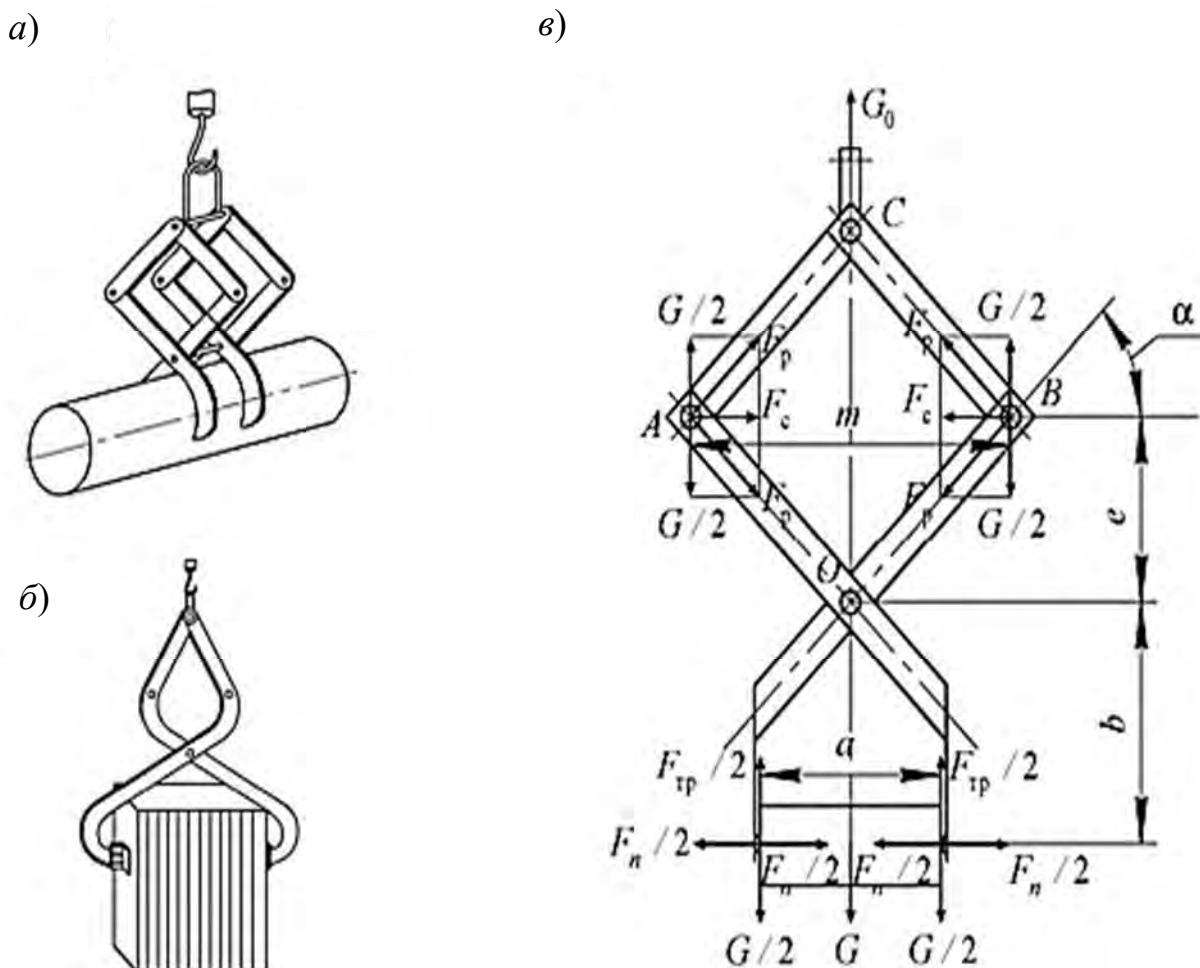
Клещевые захваты: а – для труб; б – для набора плит; в – схема сил в рычагах клещевого захвата
